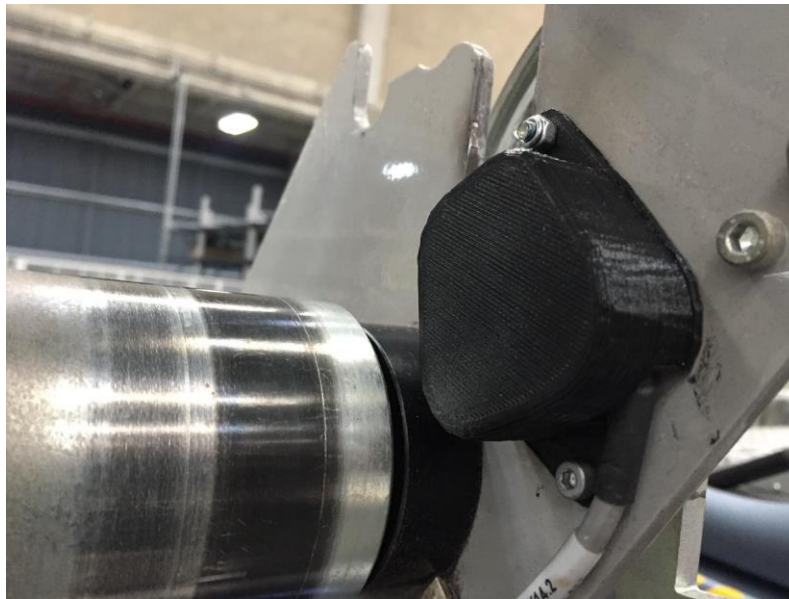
, Pieza final montada en máquina, tomada de fuente propia.
